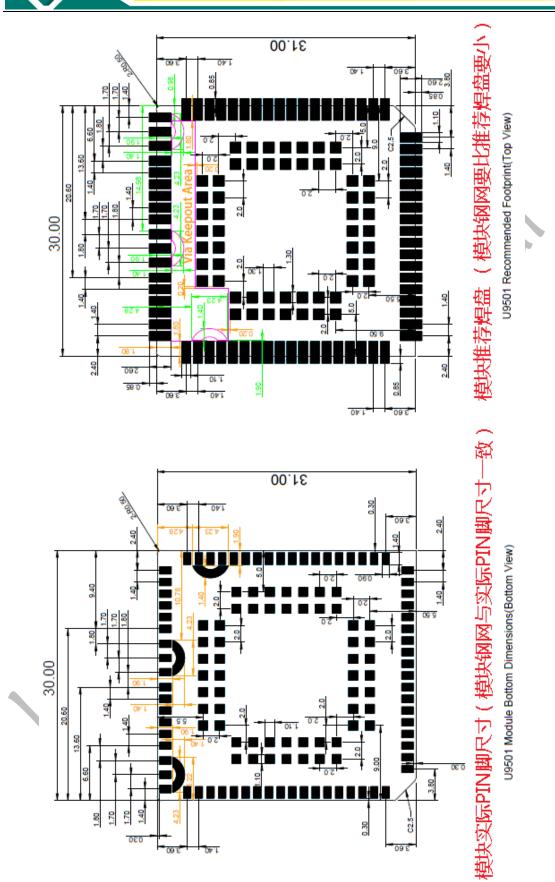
U9501 模块实际 PIN 尺寸与推荐焊盘尺寸
